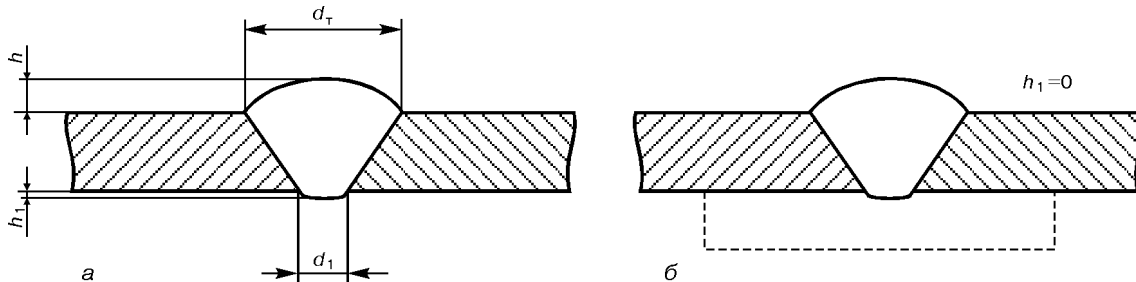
Основные параметры сварной точки при сварке на весу (а) и на съемной подкладке (б)
